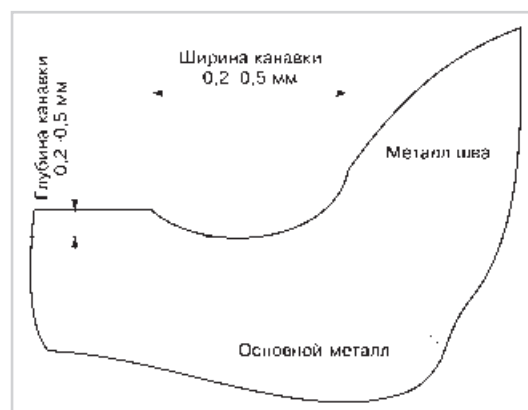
Профиль сварного шва после упрочнения ВМП зоны сплавления шва с основным металлом (Кныш В. В., Кузьменко А. З. Повышение сопротивления усталости сварных соединений высокочастотной механической проковкой // Сварщик.— 2005.—№ 2.— С.19–21)
